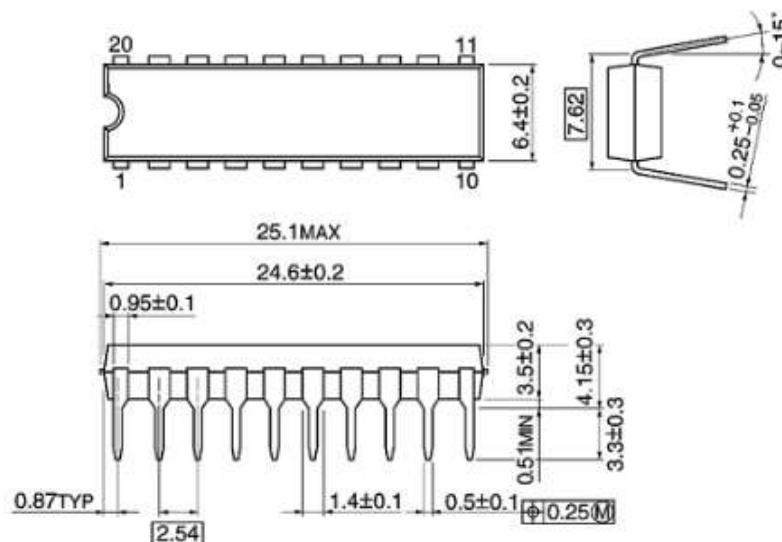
Габаритні розміри мікросхеми ATtiny2313A-PU
